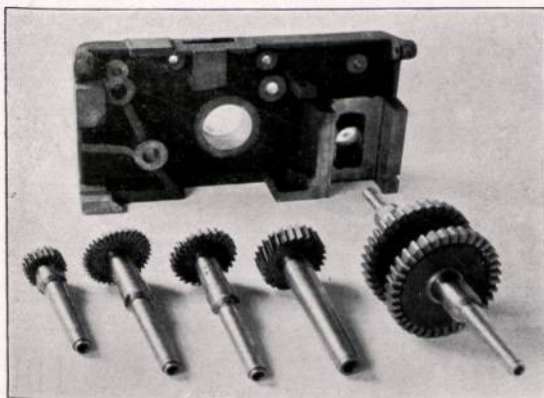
Räderplatte mit den Fräswerkzeugen für die Bearbeitung auf der Fräsmaschine.
